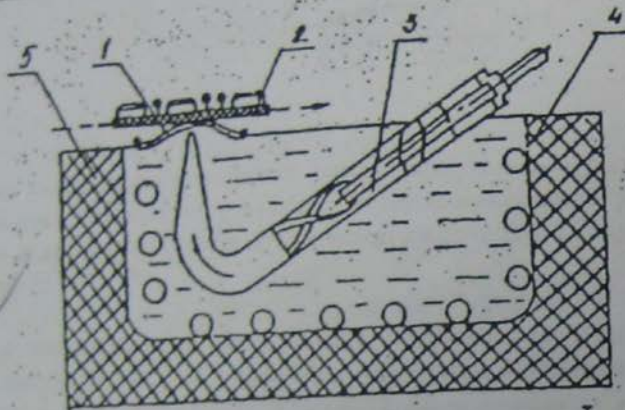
Схема установки для пайки волной припоя: 1 - волна припоя; 2 - печатная плата с установленными элементами; 3 - крыльчатка; 4 - нагреватель; 5 - ванна
